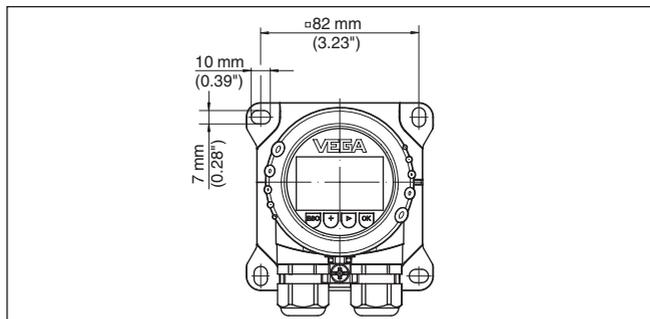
Dimensioni dei fori nel VEGADIS 82 per il montaggio a parete
